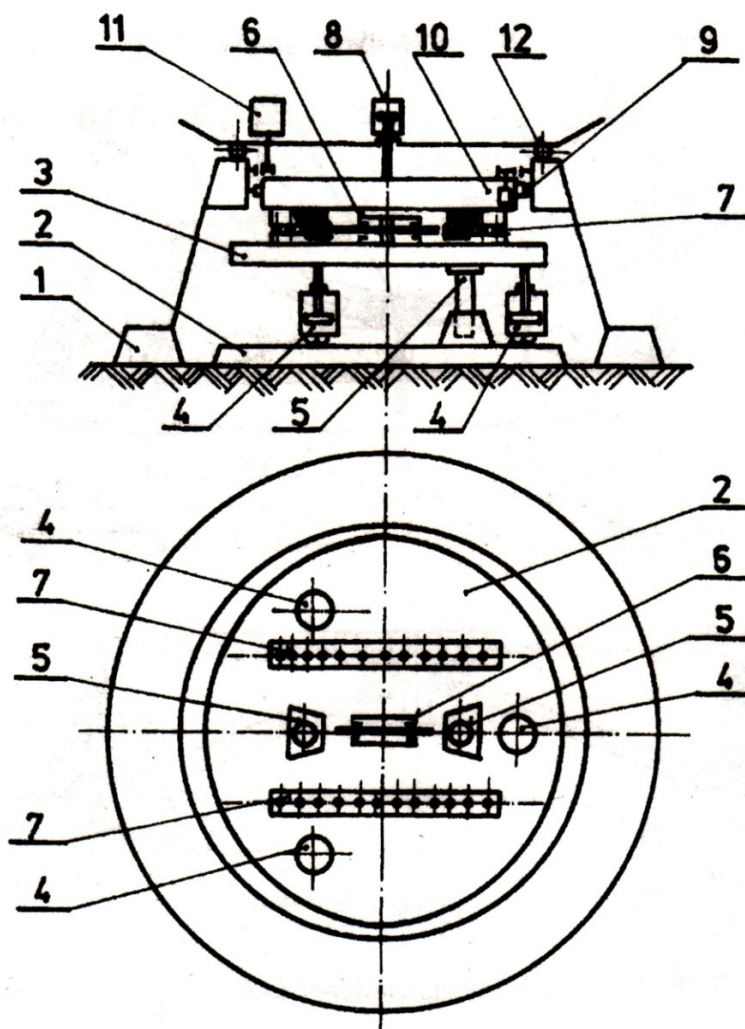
Hydraulický systém kráčení se čtyřmi hydraulickými válci
